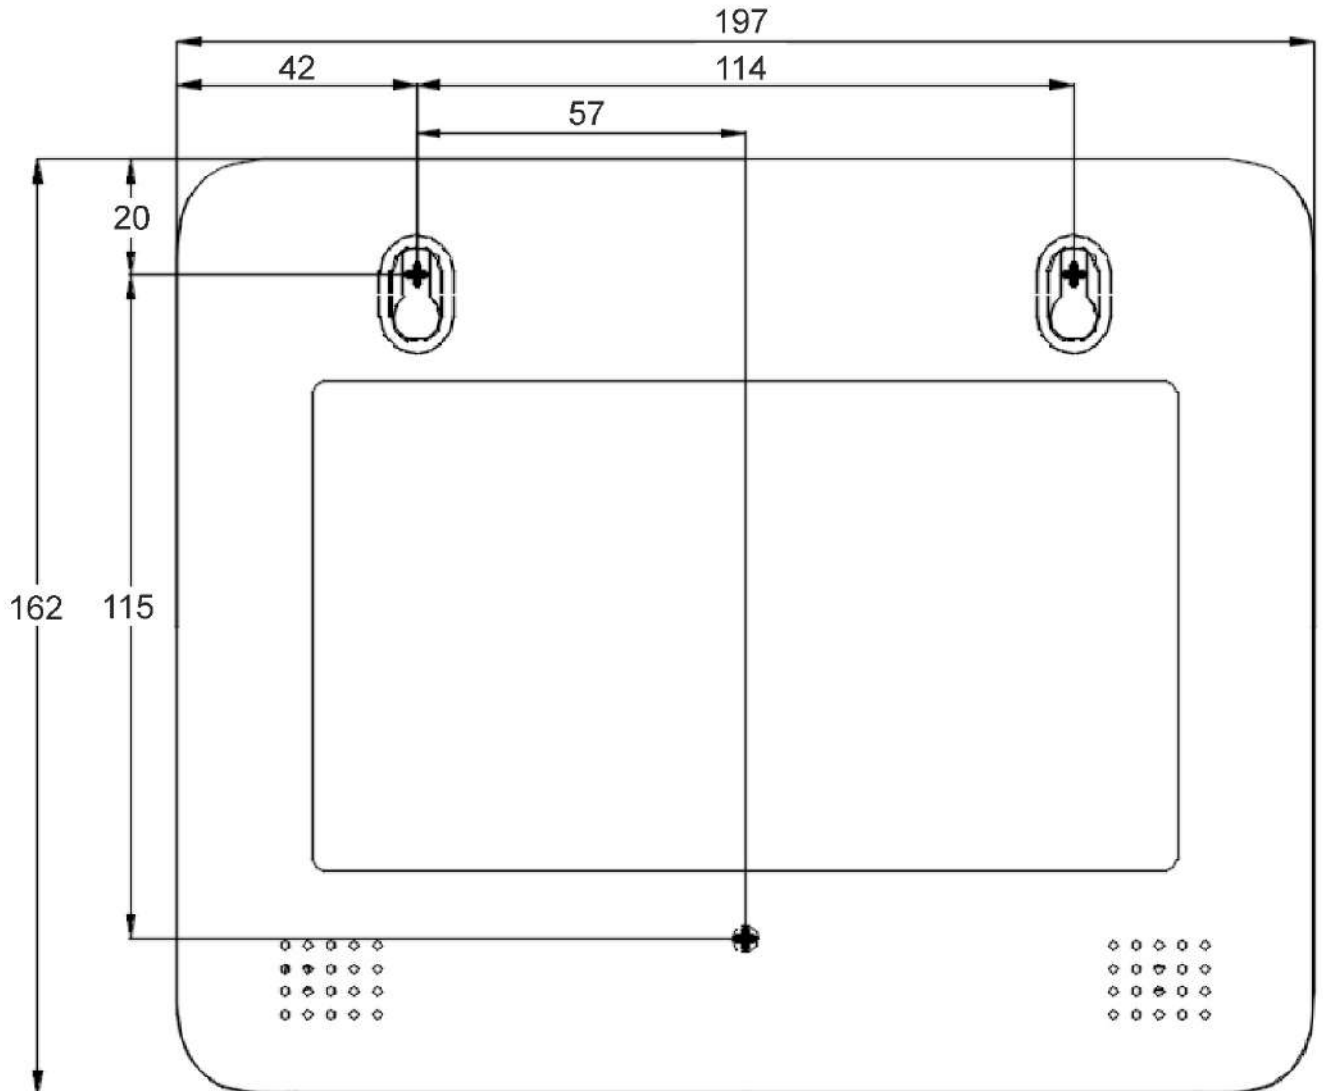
Разметка отверстий для крепления прибора КОП-04
